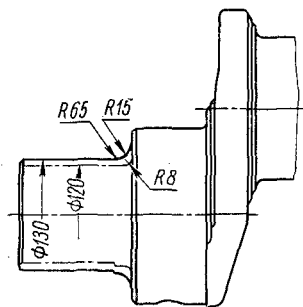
Конструкция хвостовика коленчатого вала и его усиление
